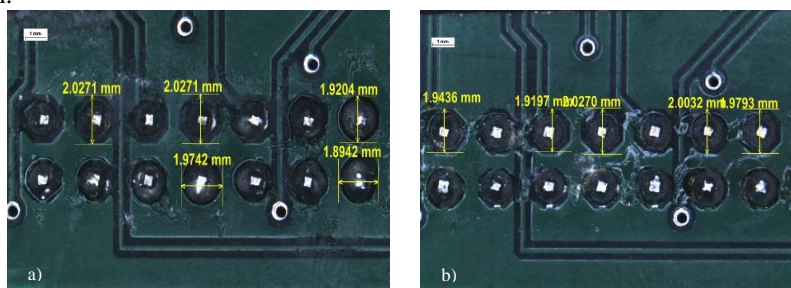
Medición de diámetros de soldadura a) muestra 1 y b) muestra 2.
